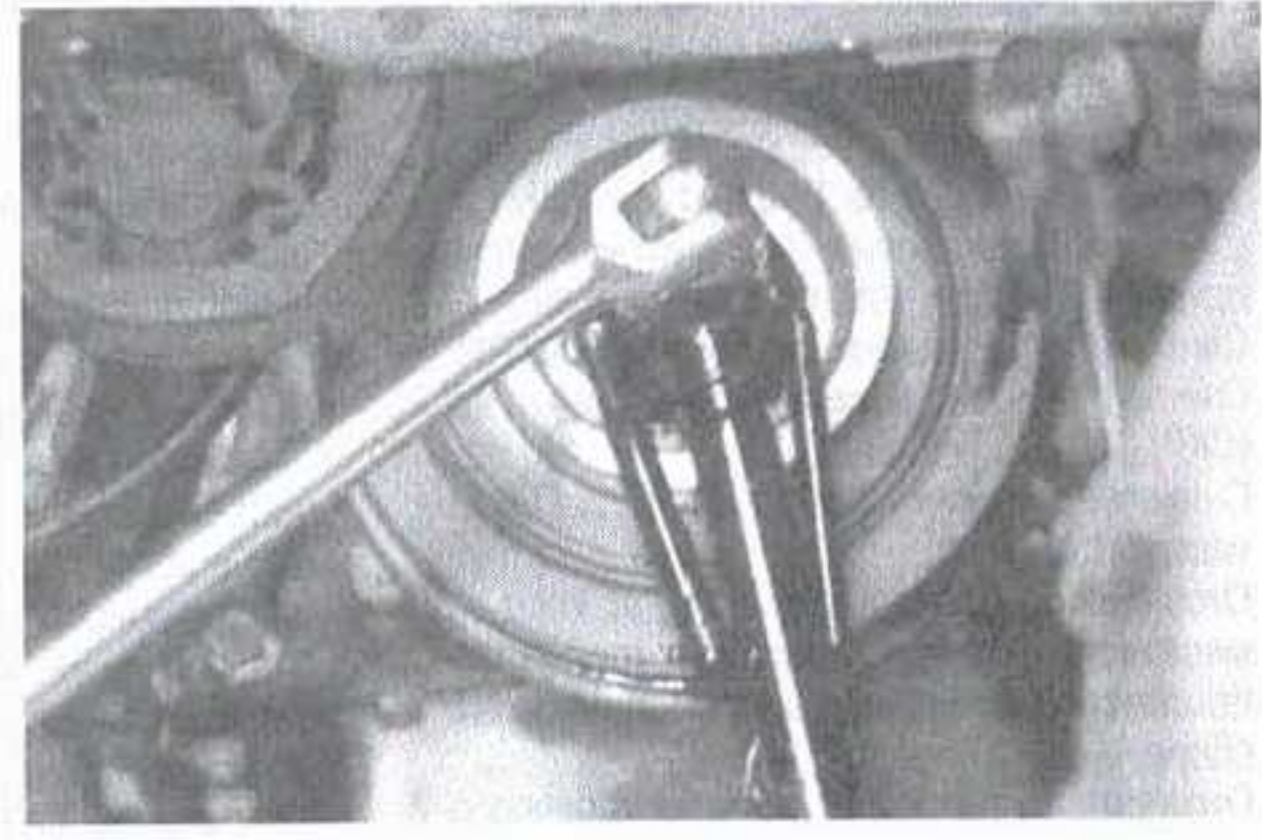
Удерживая шкив, ослабьте и отверните болт коленчатого вала против часовой стрелки
